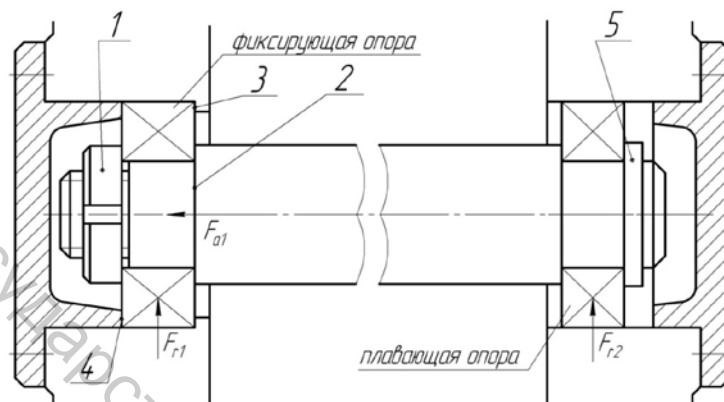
Установка подшипников в фиксирующей и плавающей опорах: 1 – шлицевая гайка со стопорной шайбой, 2 – упорный буртик на валу, 3 – упорный буртик в корпусе, 4 – торец крышки, 5 – кольцо пружинное упорное
